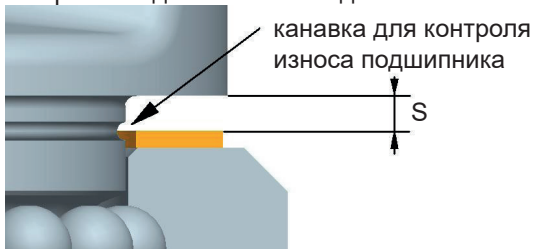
Расстояние между верхней и нижней частями корпуса и канавка для контроля износа подшипника
